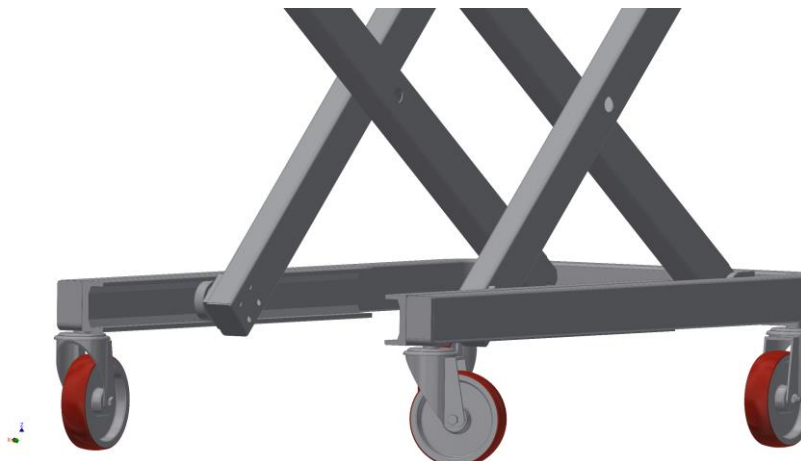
Ensamblaje sistema de elevación de tijera.
